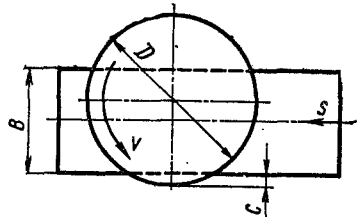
Схема смещения фрезы относительно заготовки при фрезеровании конструкционных сталей
